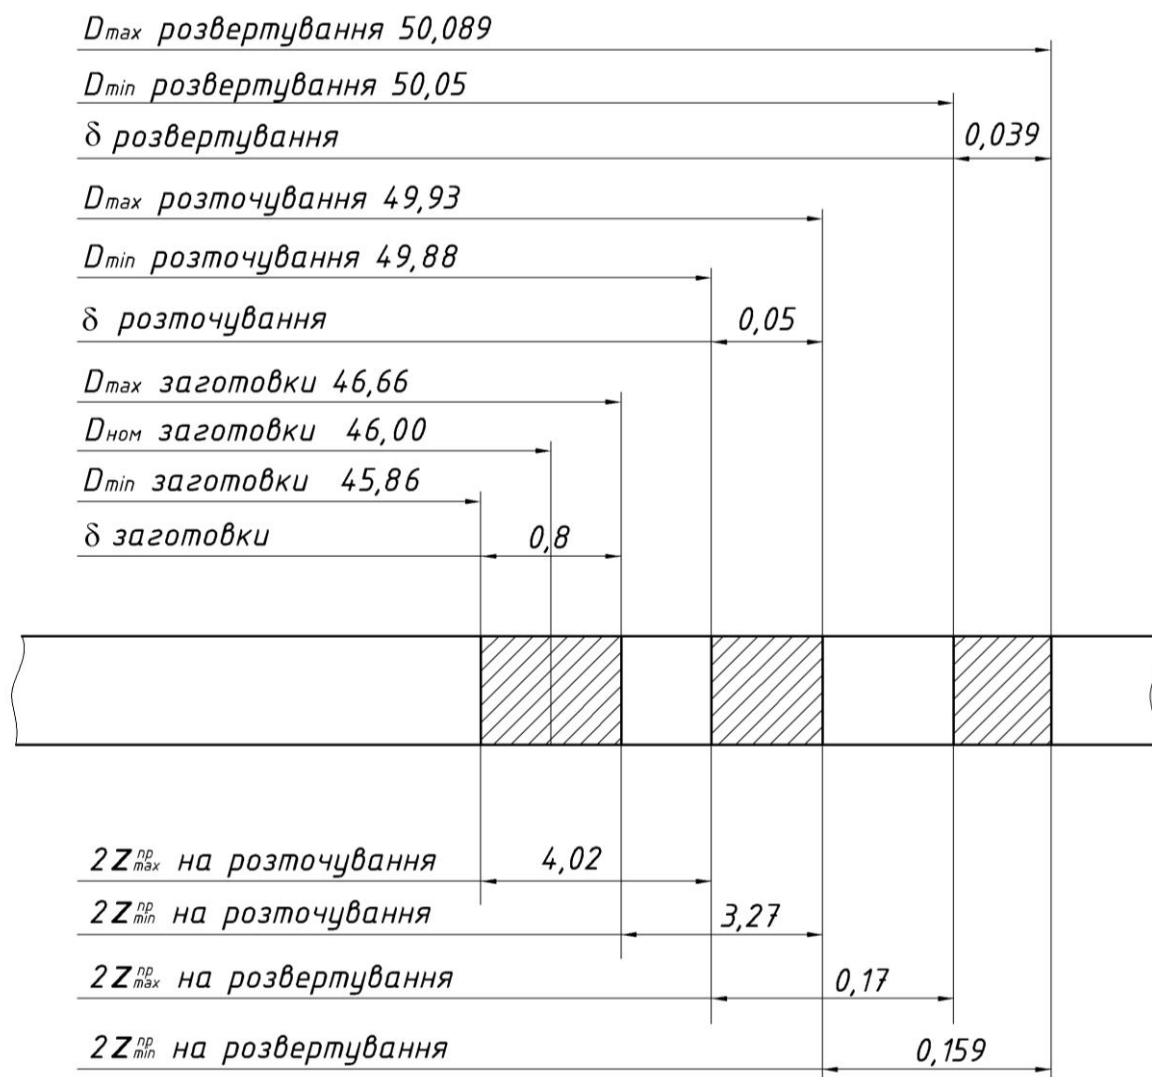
Схема графічного розташування припусків та допусків на оброблення для поверхні  $\varnothing 50E8$
